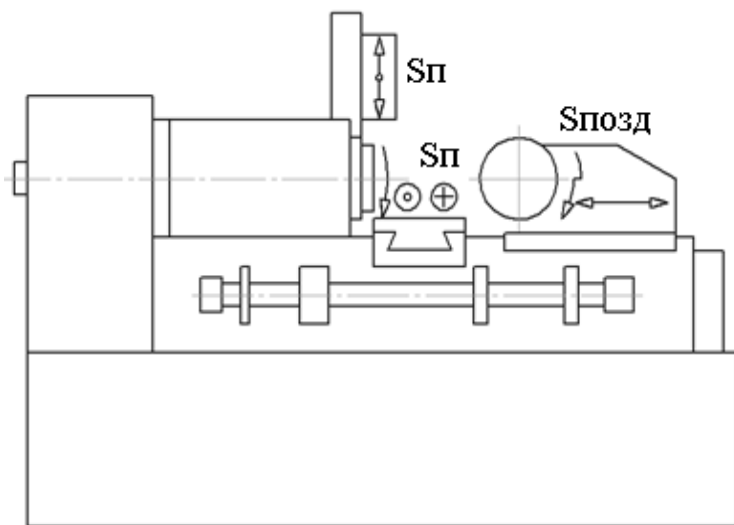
Загальний вид одношпиндельного токарно-револьверного автомата
